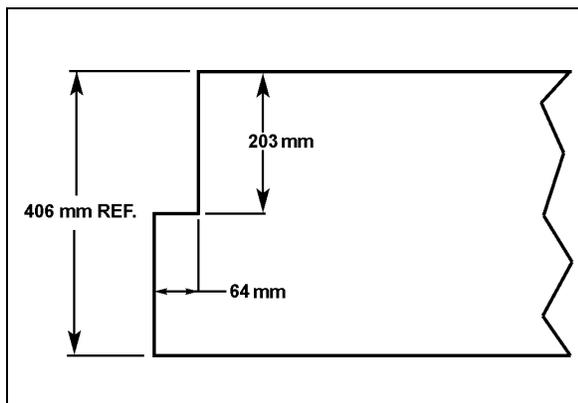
DÉCOUPAGE DU PANNEAU LATÉRAL
